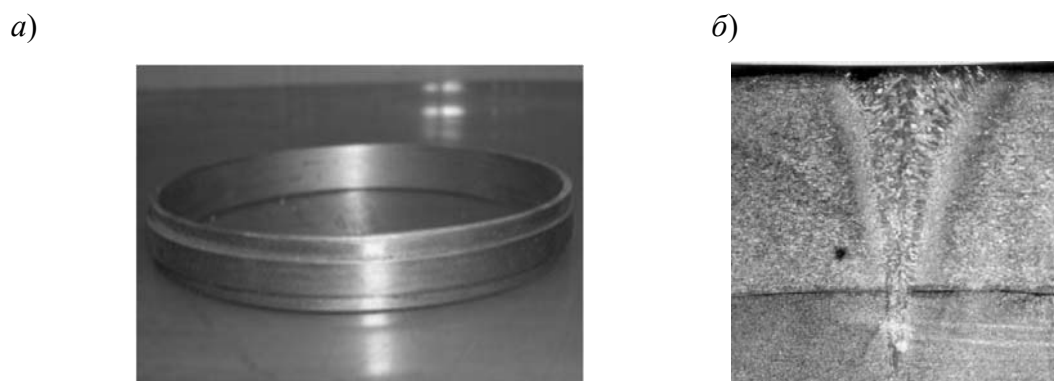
Внешний вид заготовки для изготовления токосъемного кольца из бронзы БрХ08 и стали перлитного класса (а) и макрошлиф полученного сварного соединения (б)
